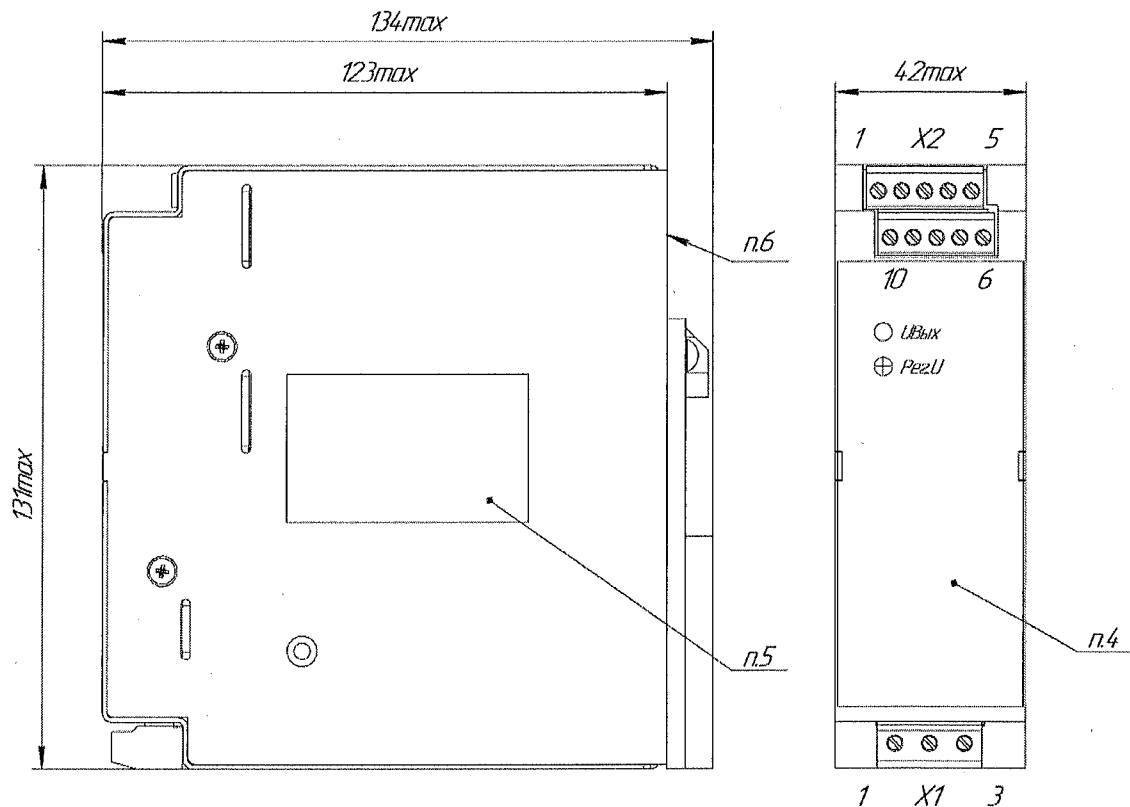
Габаритные размеры модуля КАН-Д120
